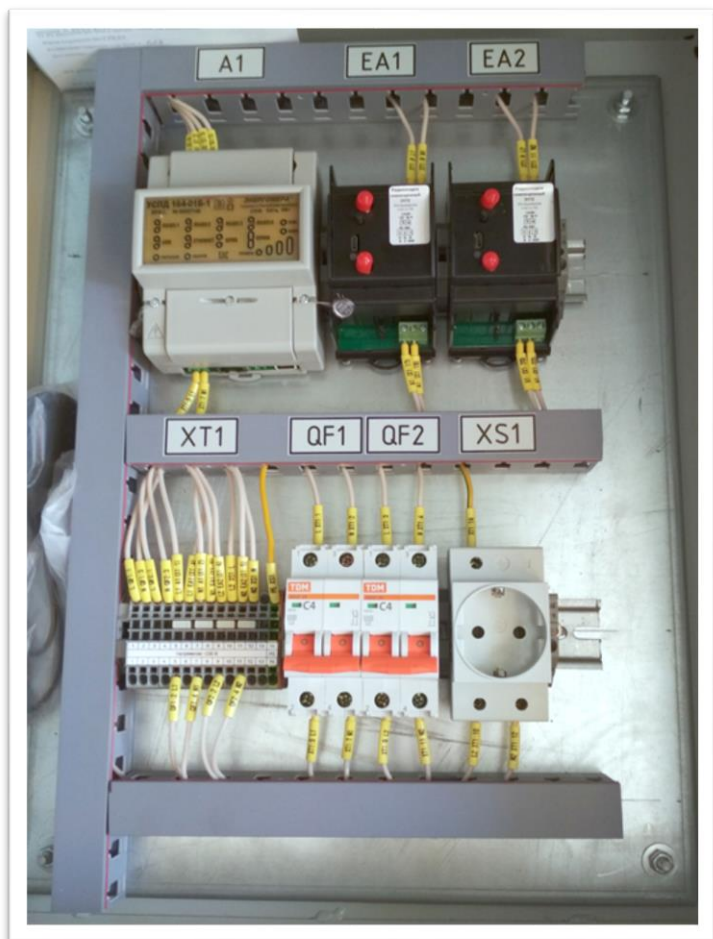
Общий вид (внутренний) и габаритные размеры шкафа АСКУЭ-2-У1
